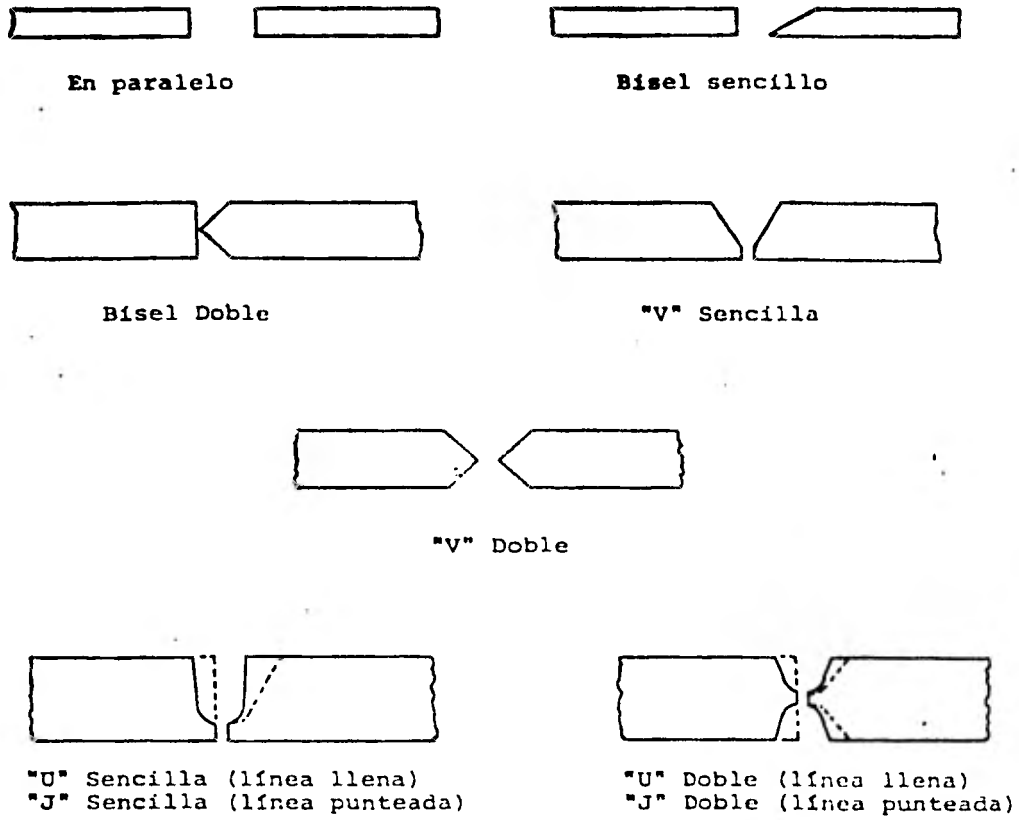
15 Formas de soldaduras de preparación
